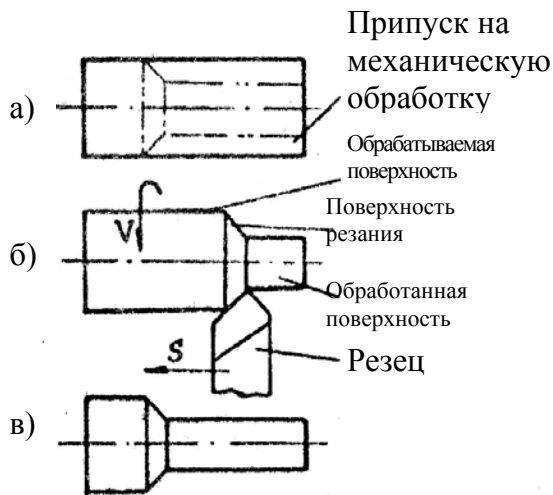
Последовательность токарной обработки: а - заготовка; б - схема обработки; в - изделие
